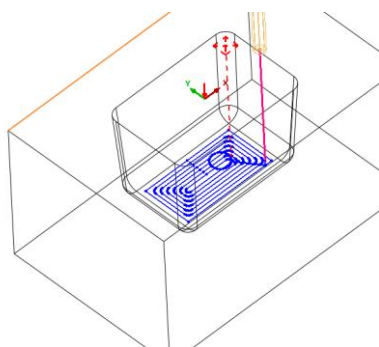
Траєкторія руху інструменту при чистовому фрезеруванні дна призматичного заглиблення
